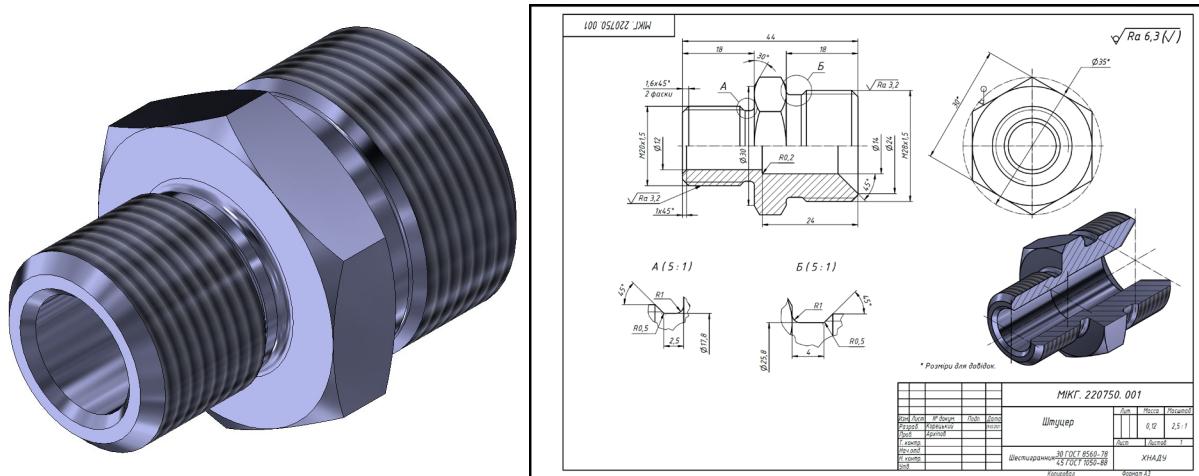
Модель та кресленик деталі типу "Штуцер", що передбачає виготовлення з прутка.
